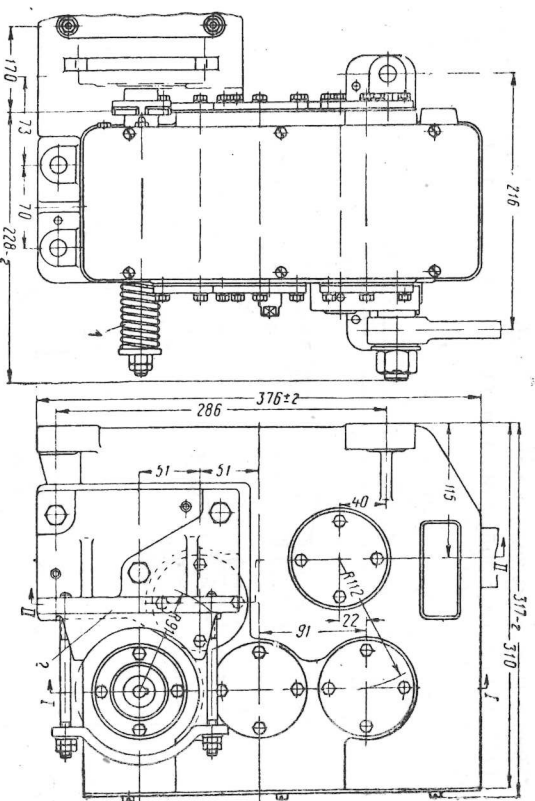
Редуктор электропривода автоматического шлагбаума (общий вид)
